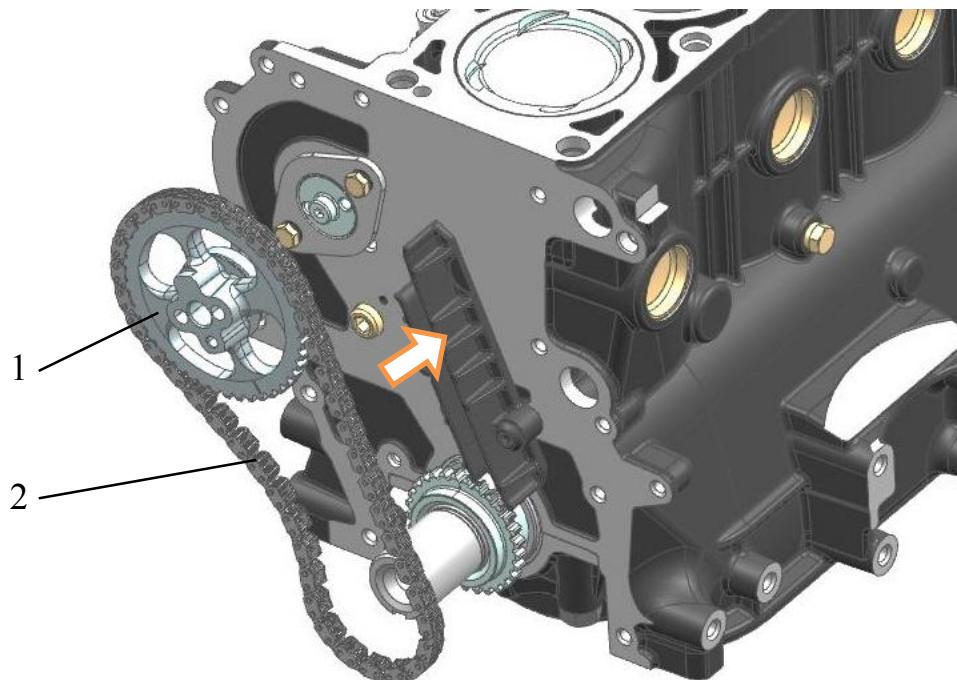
Установка нижней цепи с ведомой звездочкой промежуточного вала:
